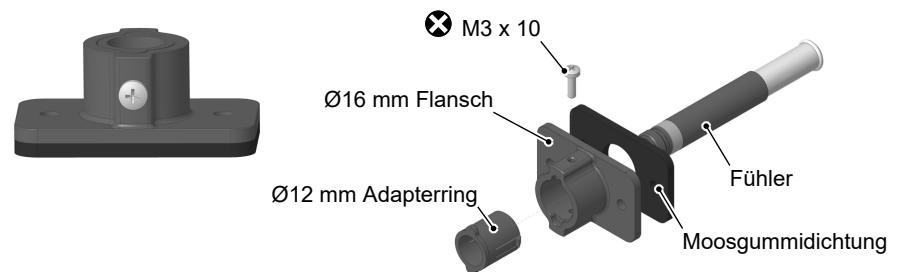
Universal Befestigungsflansch für Feuchte- und Temperaturfühler
